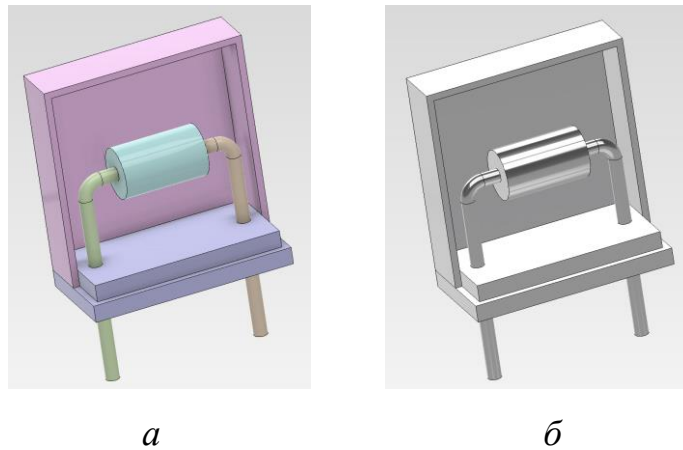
Резистор циліндричної форми з вольфраму зі сталевими контактними виводами, який розміщено в ізоляційному полімерному корпусі з кришкою:
